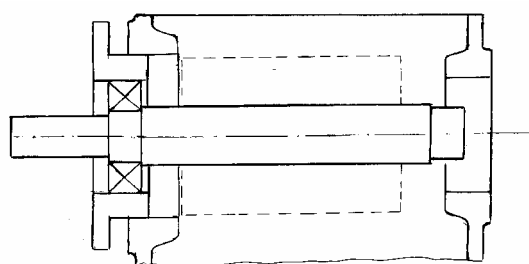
Установка вала в корпус в сборе через отверстие под стакан
